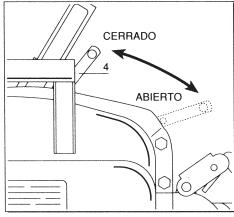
T-7 y T-13. Empuñadura de desembrague
